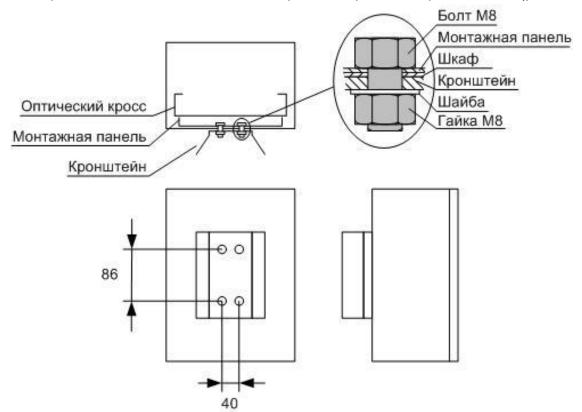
Установка кронштейна для крепления шкафа на опору
